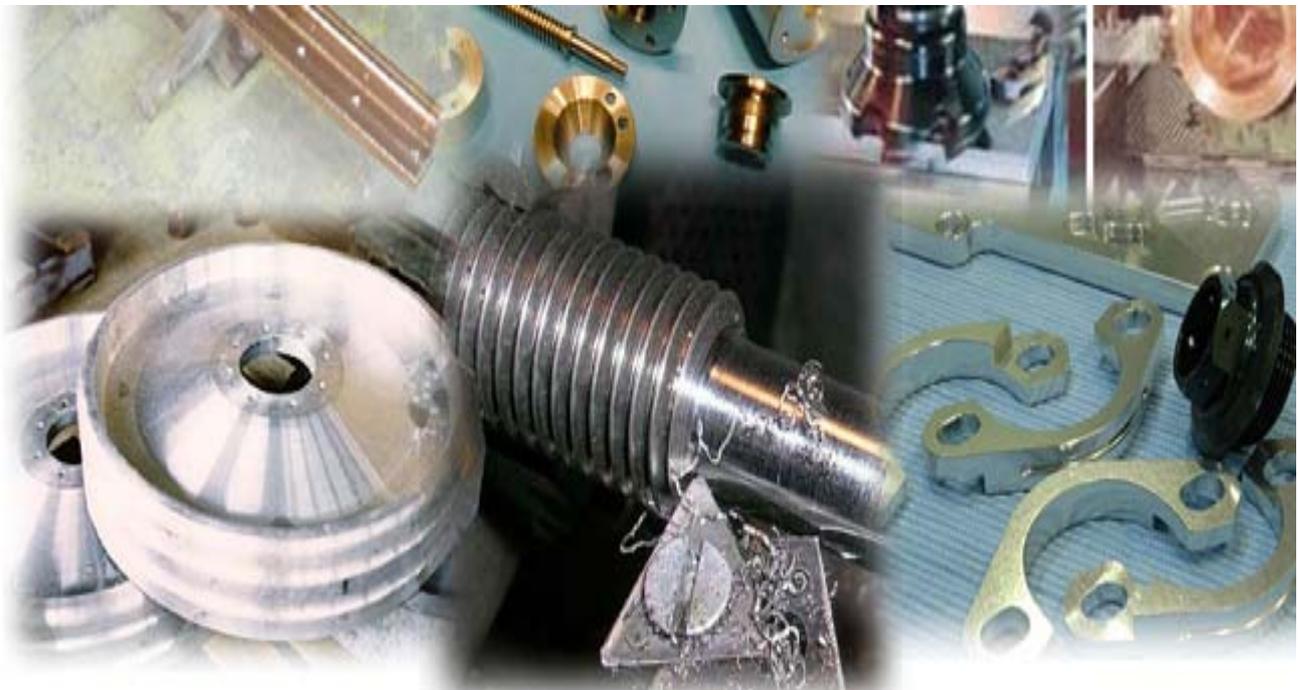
Detalle de piezas fabricadas en nuestras instalaciones
